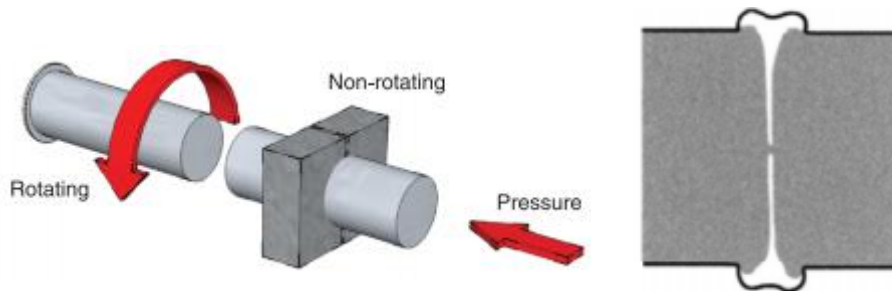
Izquierda: Fase inicial del proceso de soldeo por rotación. Gatwick Technologies Ltd, 2013. Derecha: Sección final soldada. Se muestra un collar de material externo donde la mayor parte de impurezas y contaminación es expulsada hacia el exterior [23].
